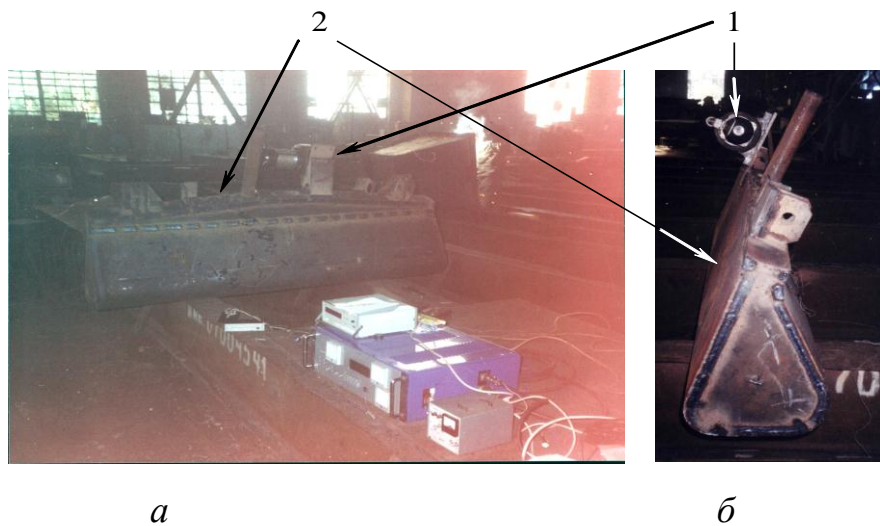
Закрепление вибратора 1 на обрабатываемой конструкции 2.
